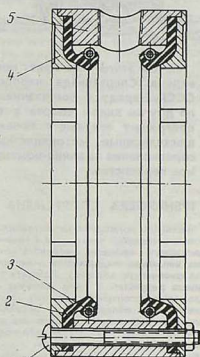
Головка подвода воздуха: 1 — винт; 2 — манжеты сальника; 3 — пружина манжеты; 4 — крышка; 5 — корпус.
